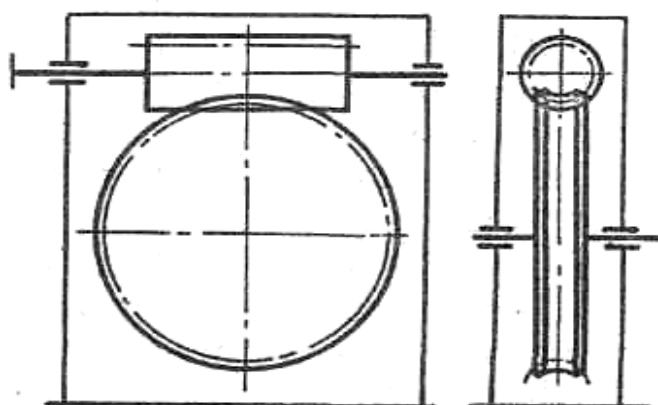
Схема червячного редуктора с горизонтальным расположением червяка над колесом (редуктор типа РЧН)
